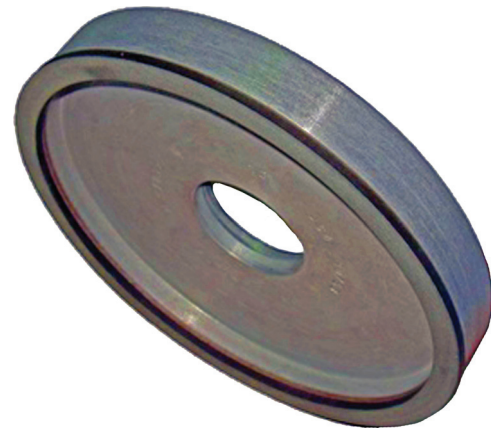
Круг алмазный плоскошлифовальный типа 6A2
